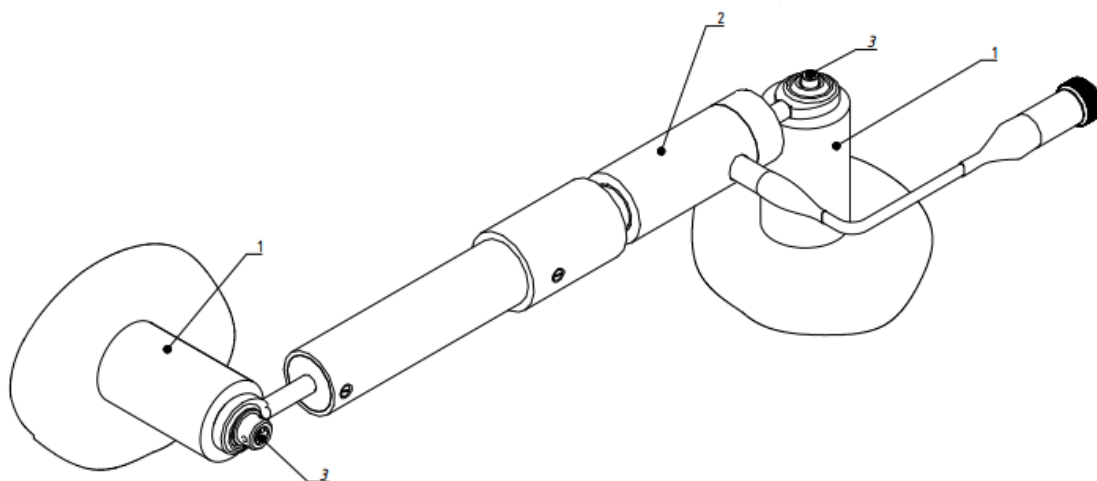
Общий вид установки датчика преобразователя ВК-318.30
